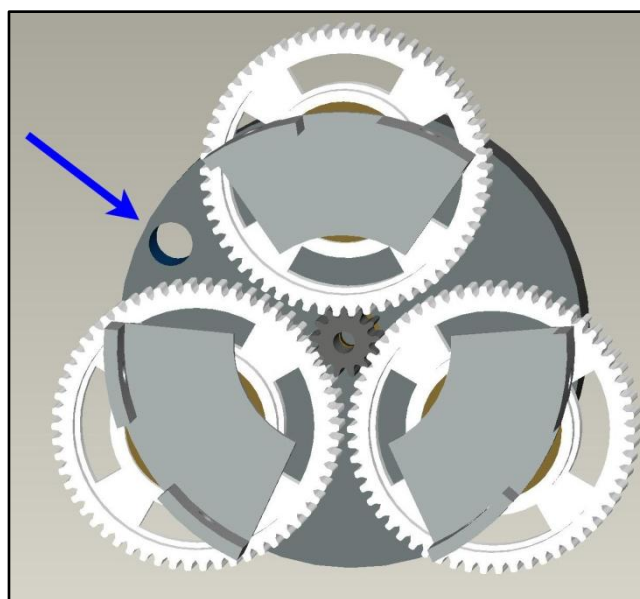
Hueco entre los engranajes para ajustar el tubo con refrigerante.
